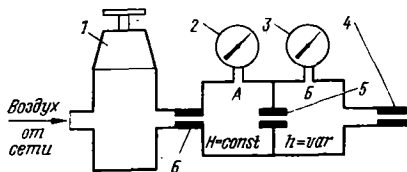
Принципиальная схема пневматического контрольного прибора
